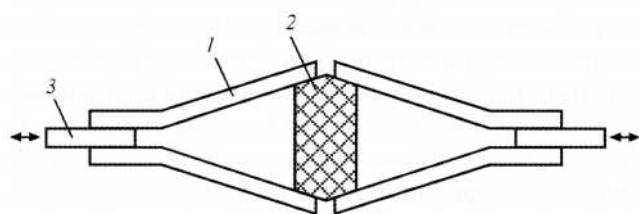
Схема составного образца для малоциклового испытания сварных соединений с угловой деформацией: 1 — испытываемые элементы; 2 — демпфер; 3 — элемент для закрепления в пульсаторе.
